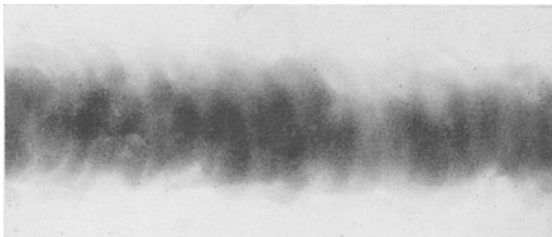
Röntgenbild einer guten Aluminiumblechschweißung (ungehämmert).
